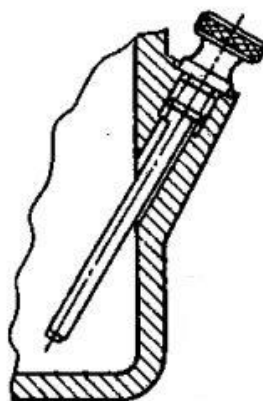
Эскиз жезлового маслоуказателя (установка в нижней части корпуса редуктора)
